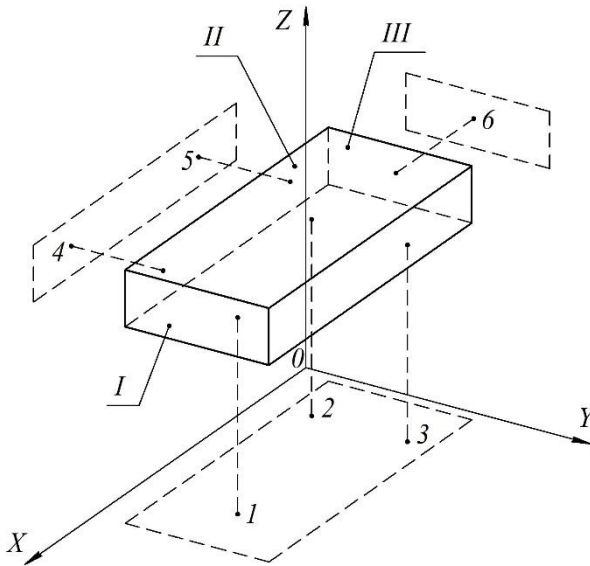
Комплект баз призматичної деталі: I, II, III – бази деталі
